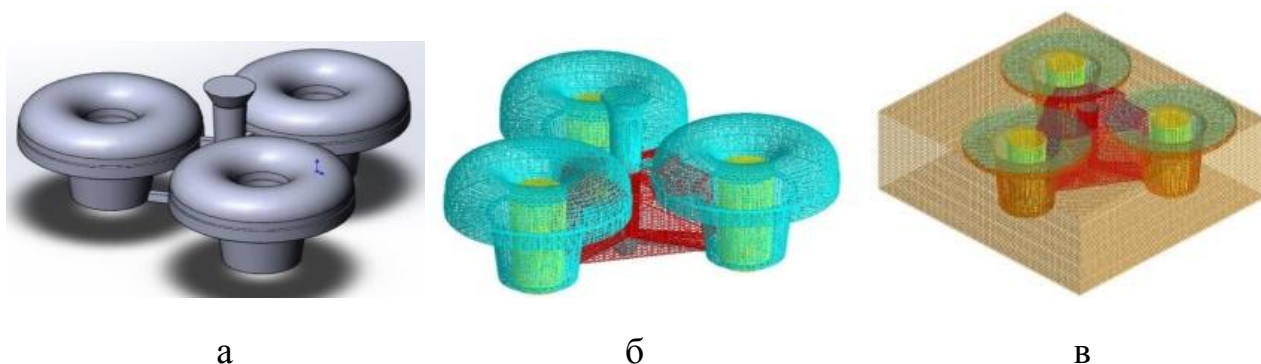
Модельное представление: отливка «Корпус» с системой питания (а); конечно-разностная сетка отливки с СП (б) и конструкция литейной формы (в)
